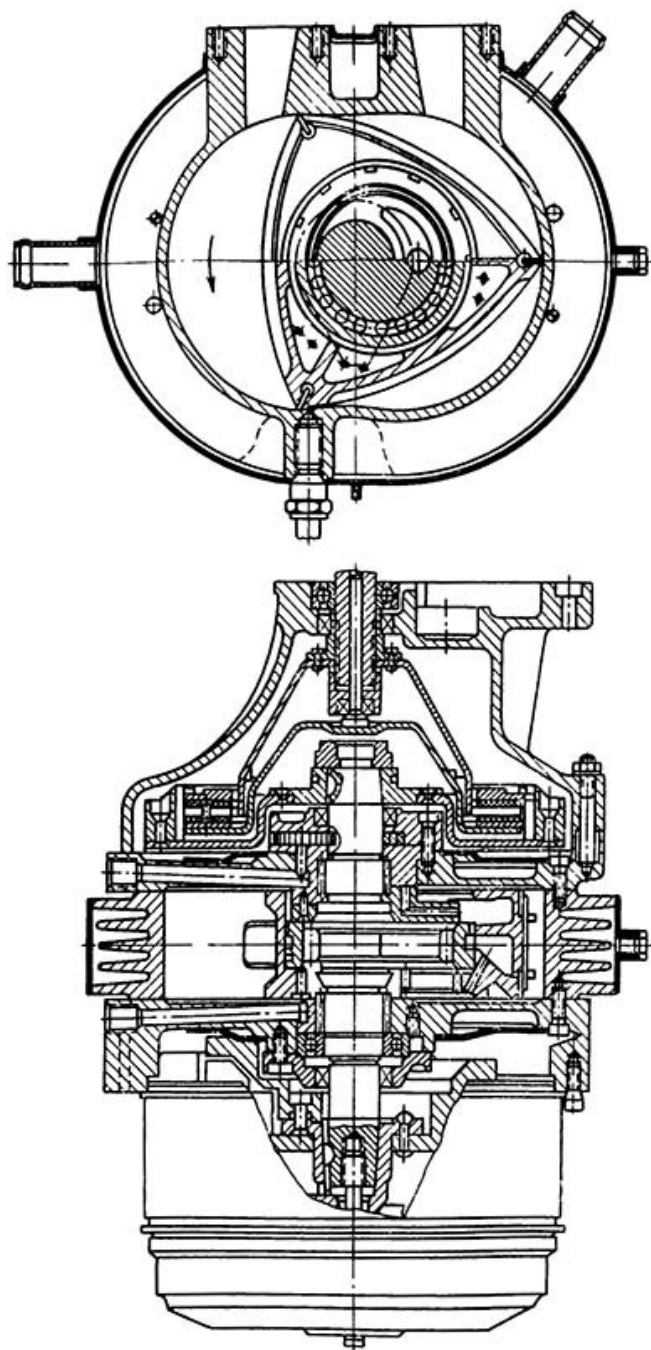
Продольный и поперечный разрезы двигателя ККМ-150W (автомобильный вариант)
